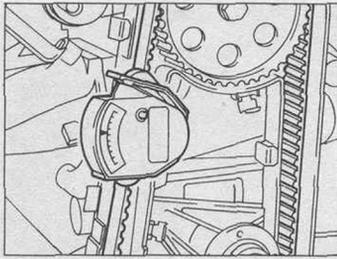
Проверка натяжения зубчатого ремня привода (Глава 16)
